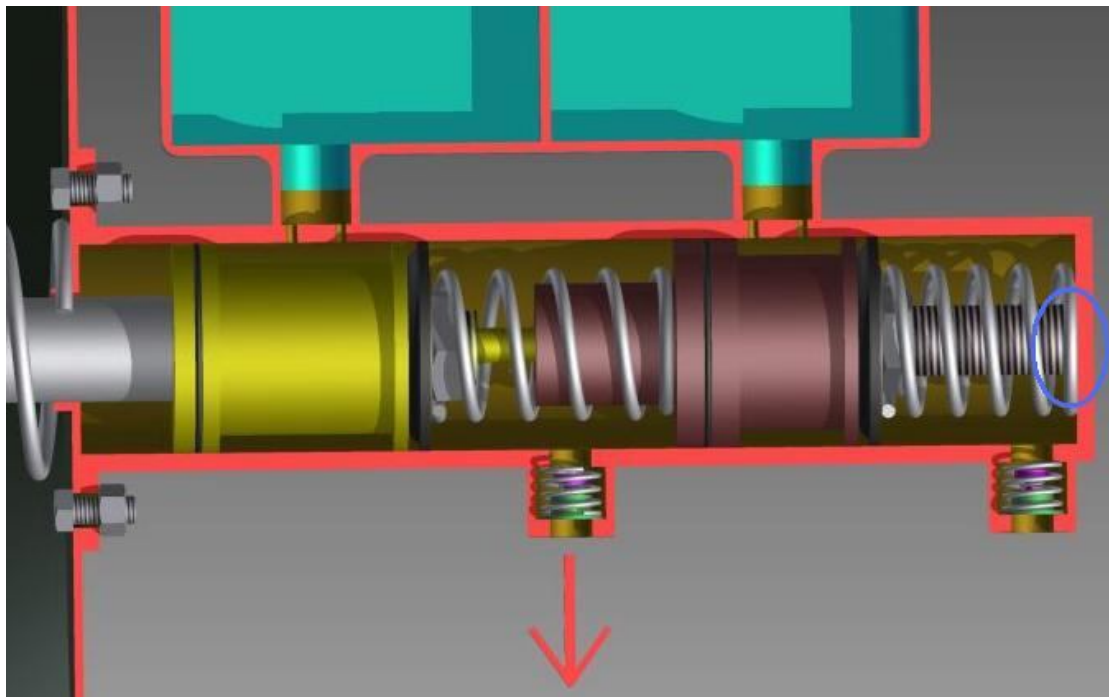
Hlavní brzdový s poruchou prvního okruhu
